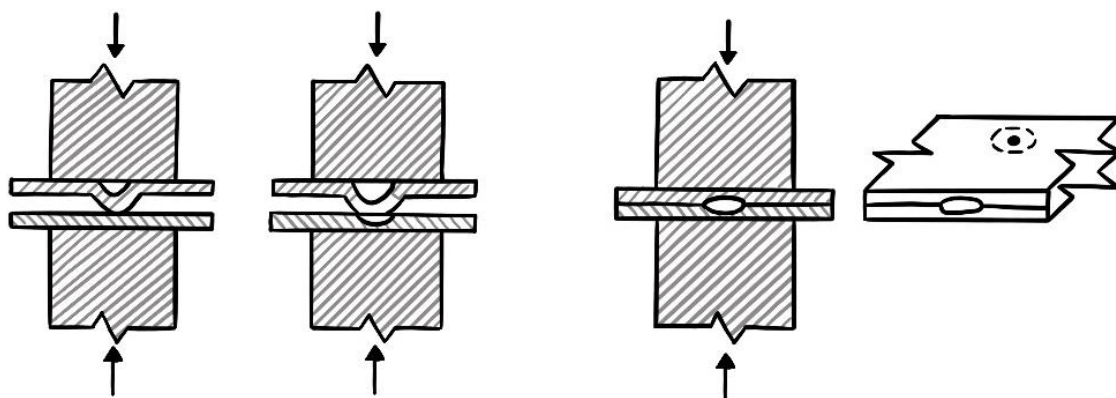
Processo de Soldadura de pontos por projeção. Adaptado de [27]
